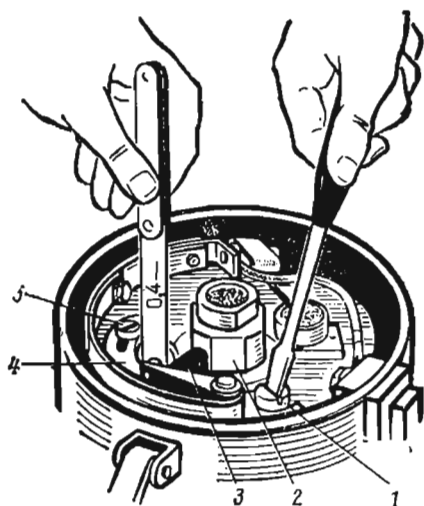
Проверка и регулировка зазора между контактами прерывателя
